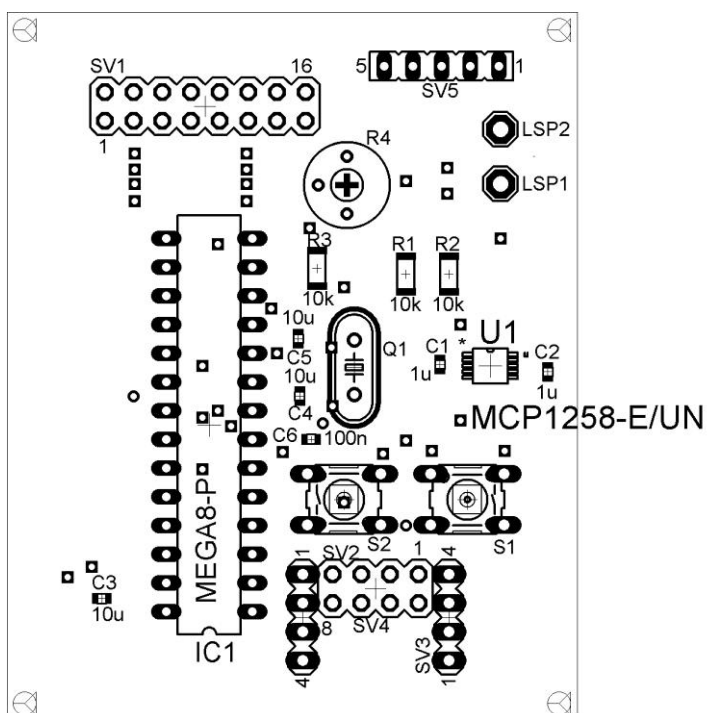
PCB luxmetra, strana: TOP, 62,4 x 50,5 mm, M 1:1
